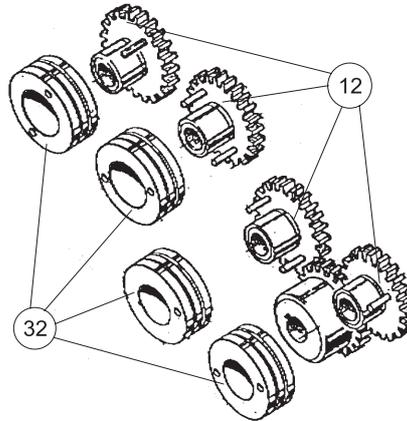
/7b Ersatzrollen Aluminium / Spare aluminium rolls
